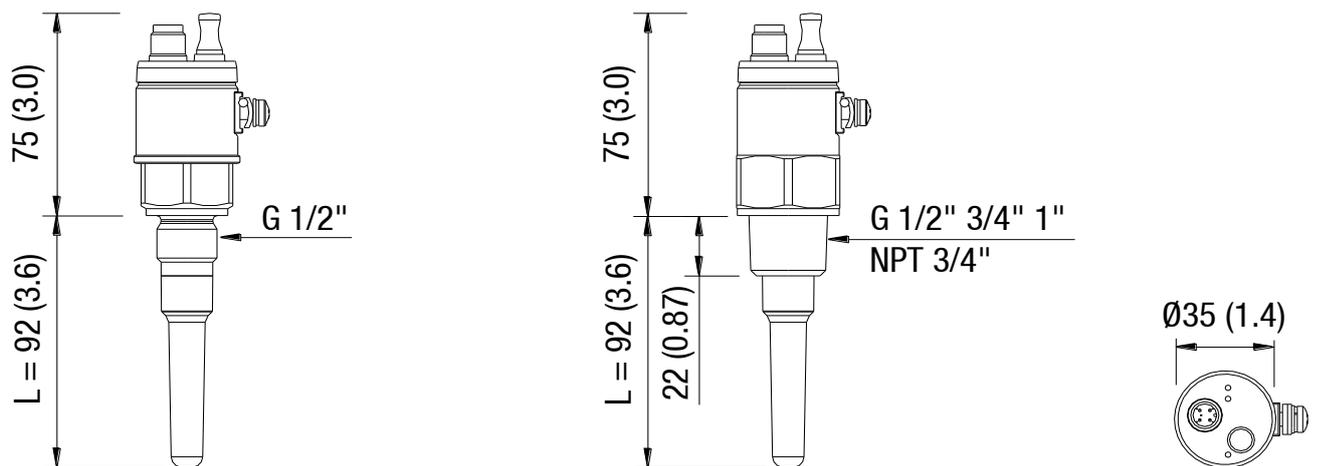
Abmessungen CN 7120, Gehäuse Ø 35 mm
